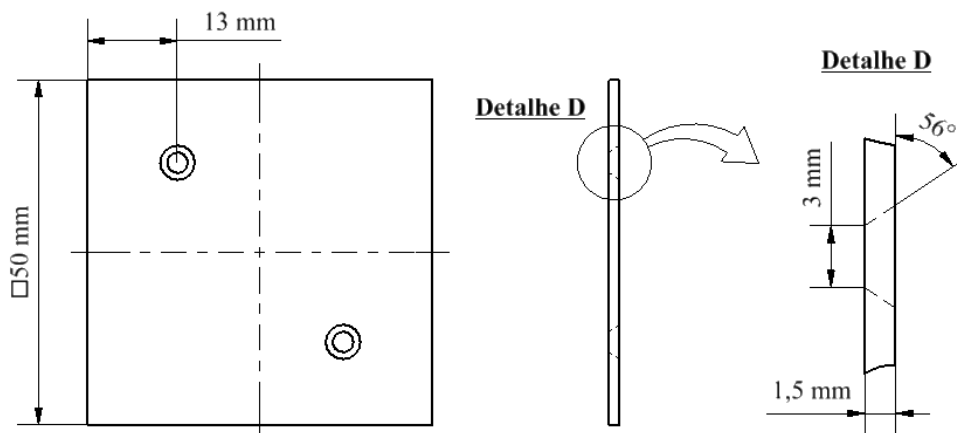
Dimensões e detalhes da tampa do aquecedor.
